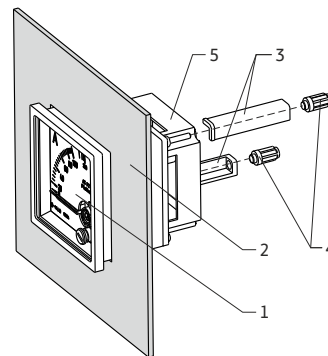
Схема установки прибора: на рисунке обозначены: 1 - прибор; 2 - панель/дверь НКУ; 3 - пластиковый фиксатор; 4 - пластиковая гайка; 5 - защитная клеммная крышка.
